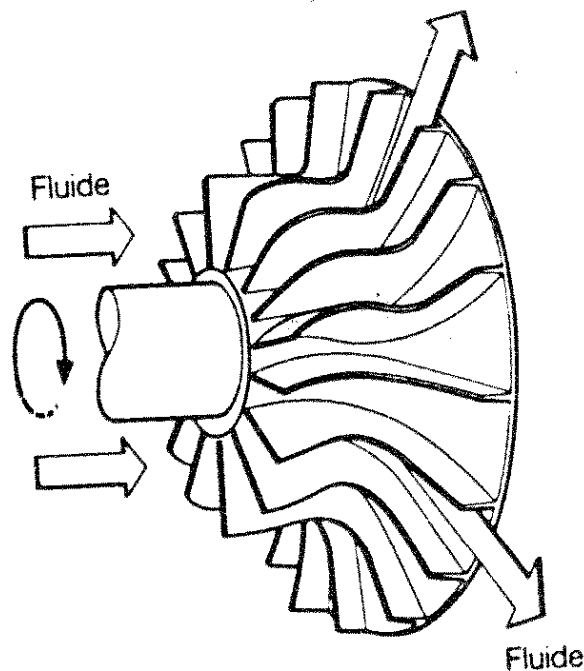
Grille d'aubes d'un compresseur centrifuge
